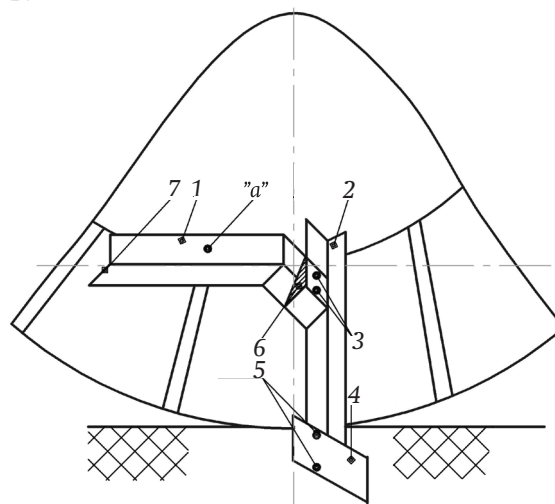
Устройство противоскольжения, закрепленное к диску обода колеса: 1 – кронштейн; 2 – стойка; 3 – болты; 4 – грунтозацеп; 5 – болтовое соединение; 6 – ребро жесткости; 7 – резиновая прокладка
